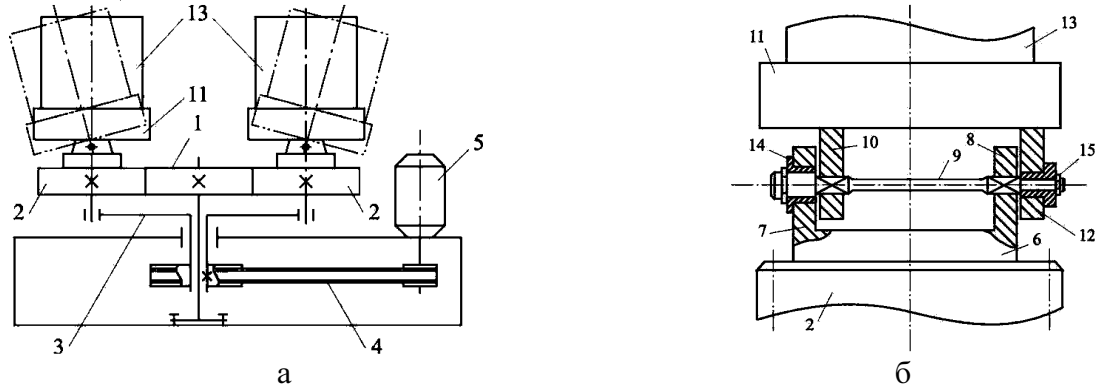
Багатокамерна відцентрово-вібраційна установка, а – загальний вигляд, б - механізм коливання
